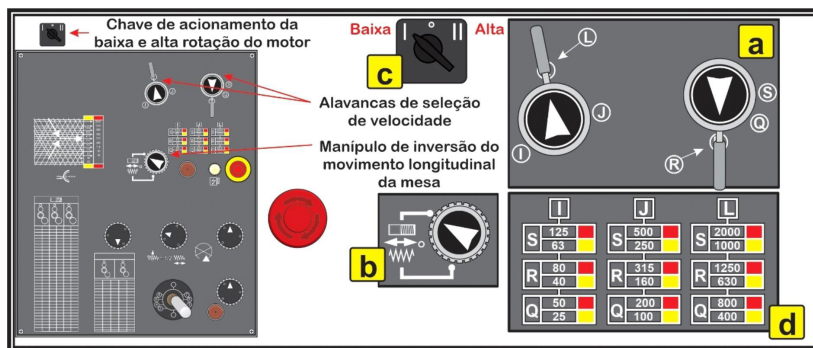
Elementos de seleção e ajuste de rotação (rpm) no torno mecânico
